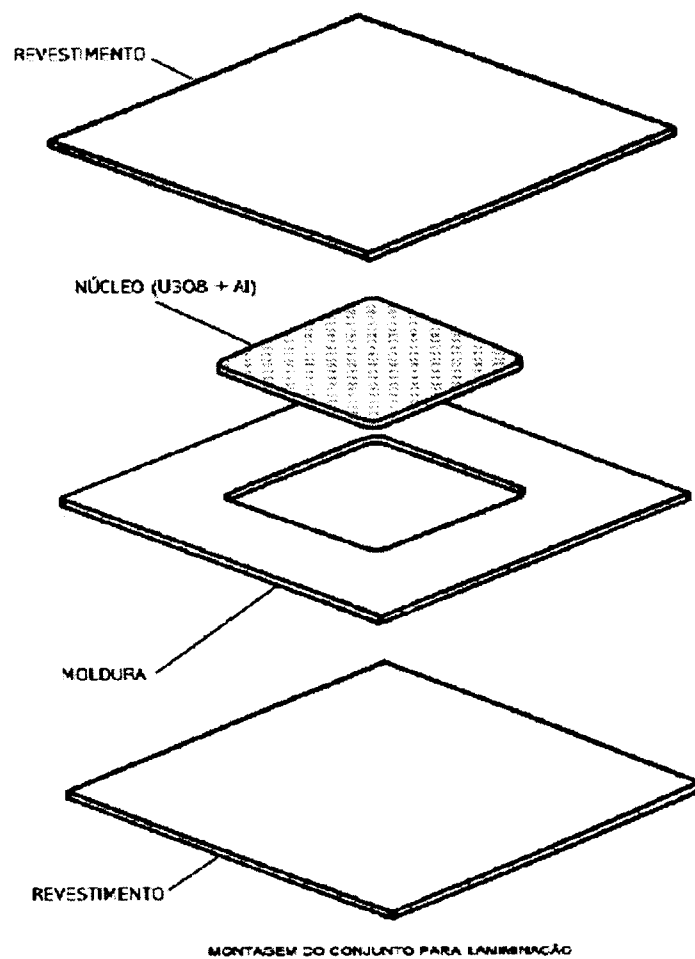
Esquema de montagem do conjunto a ser laminado.
